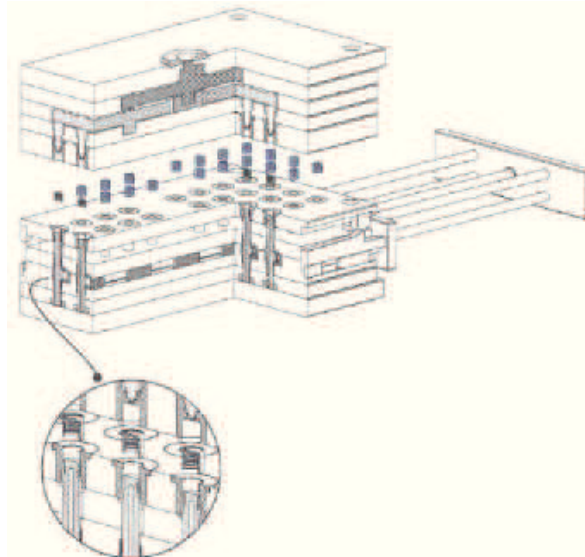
Molde com núcleo rotativo com cremalheiras e rodas dentadas [16].
